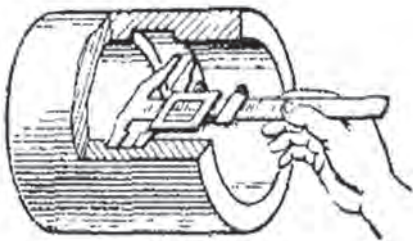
Вимірювання ширини внутрішньої канавки штангенциркулем
